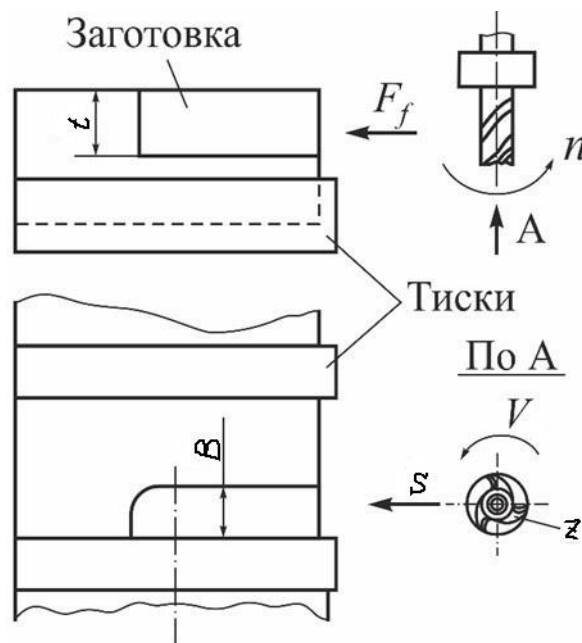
Схема фрезерования уступа в заготовке из алюминиевого сплава фрезой диаметром D_ϕ с количеством зубьев Z
